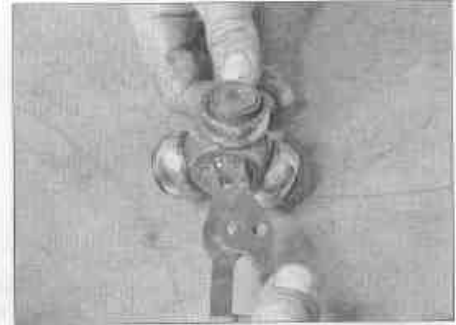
Снимите стопорное кольцо с помощью щипцов для снятия и установки стопорных колец
